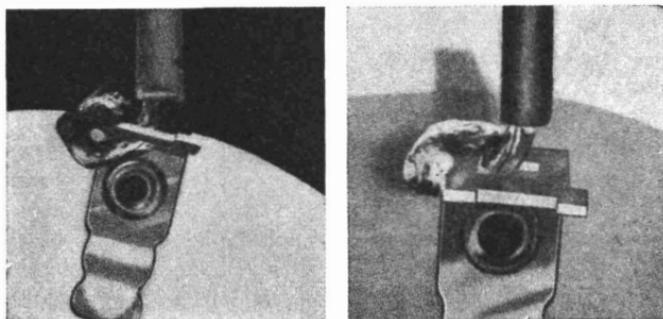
A sinistra, saldatura fatta male; a destra, saldatura fatta bene.
